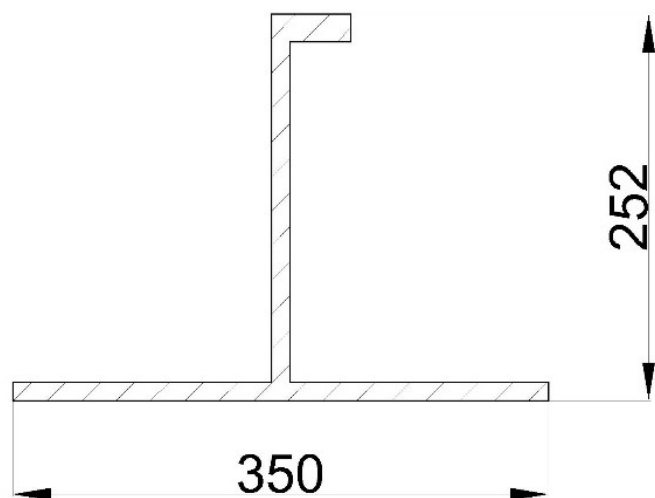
Наближений переріз профілю шпангоута з приєднаним пояском для варіанта конструкції борту з подовженими проміжними шпангоутами
